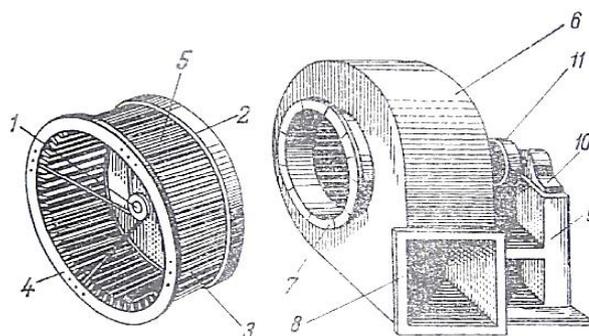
Конструктивное устройство центробежного вентилятора.
